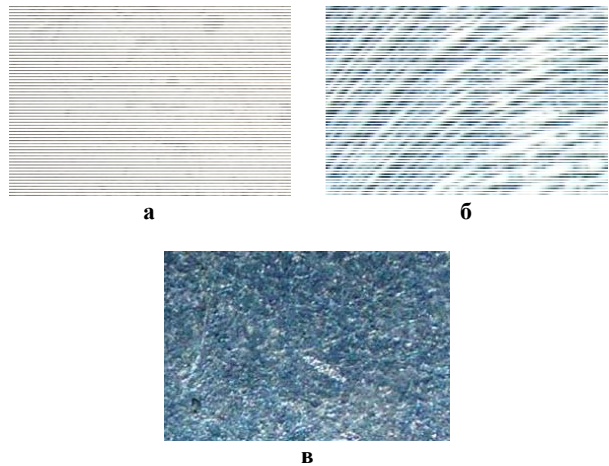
Зовнішній вигляд поверхонь дюралюмінієвих зразків: а – калібрований прокат; б – після точіння; в – після вібраційного шліфування
